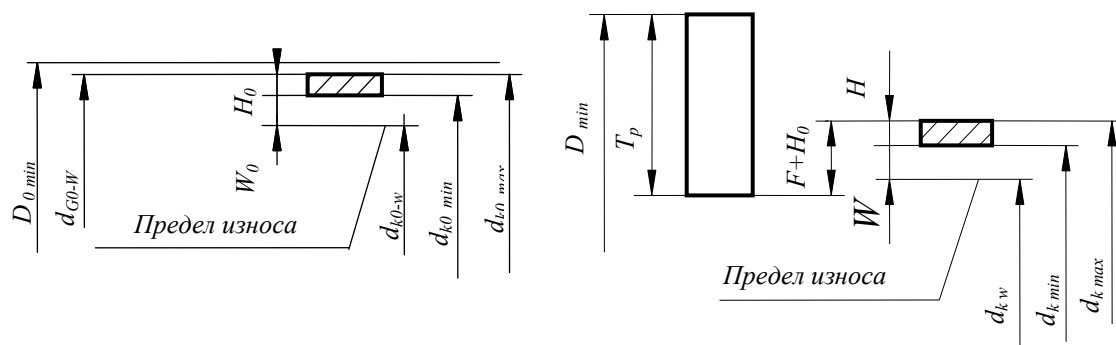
Схемы расположения полей допусков калибров для контроля расположения поверхностей с базовыми измерительными элементами (при T_P до 300мкм)
